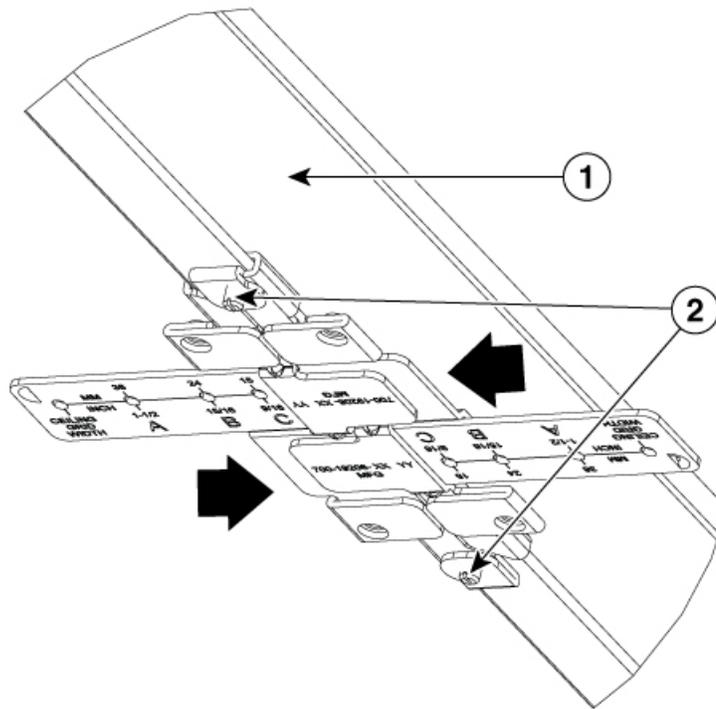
Attaches de plafond complètement ouvertes [AIR-AP-T-RAIL-F]
